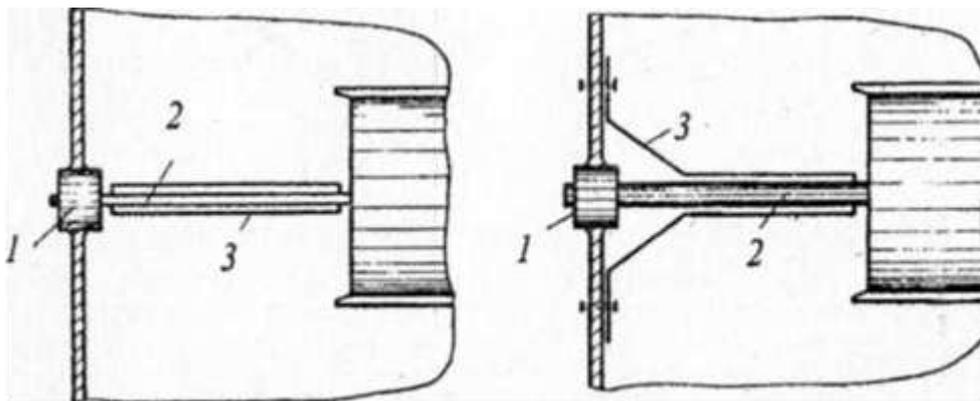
Защита вала от наматывания волокнистых материалов: а - свободно насаженной цилиндрической втулкой; б - неподвижной конусной втулкой; 1 - подшипник; 2 - вал; 3 - защитная втулка
